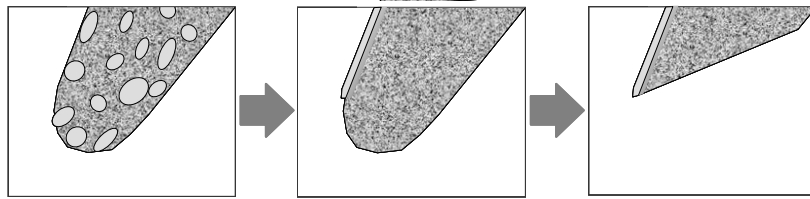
Übertragung des natürlichen Prinzips der Verschleißlenkung auf technische Schneidwerkzeuge ausgehend vom Stand der Technik
